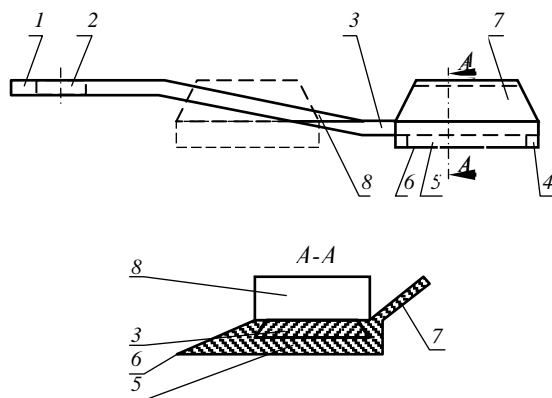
Нож косилки-измельчителя со съемной режущей частью: 1 – внутренний участок пластины; 2 – отверстие для крепления; 3 – периферийный участок пластины; 4 – выступ; 5 – режущая накладка; 6 – боковая режущая кромка; 7 – подъемная пластинка; 8 – средний наклонный участок пластины
